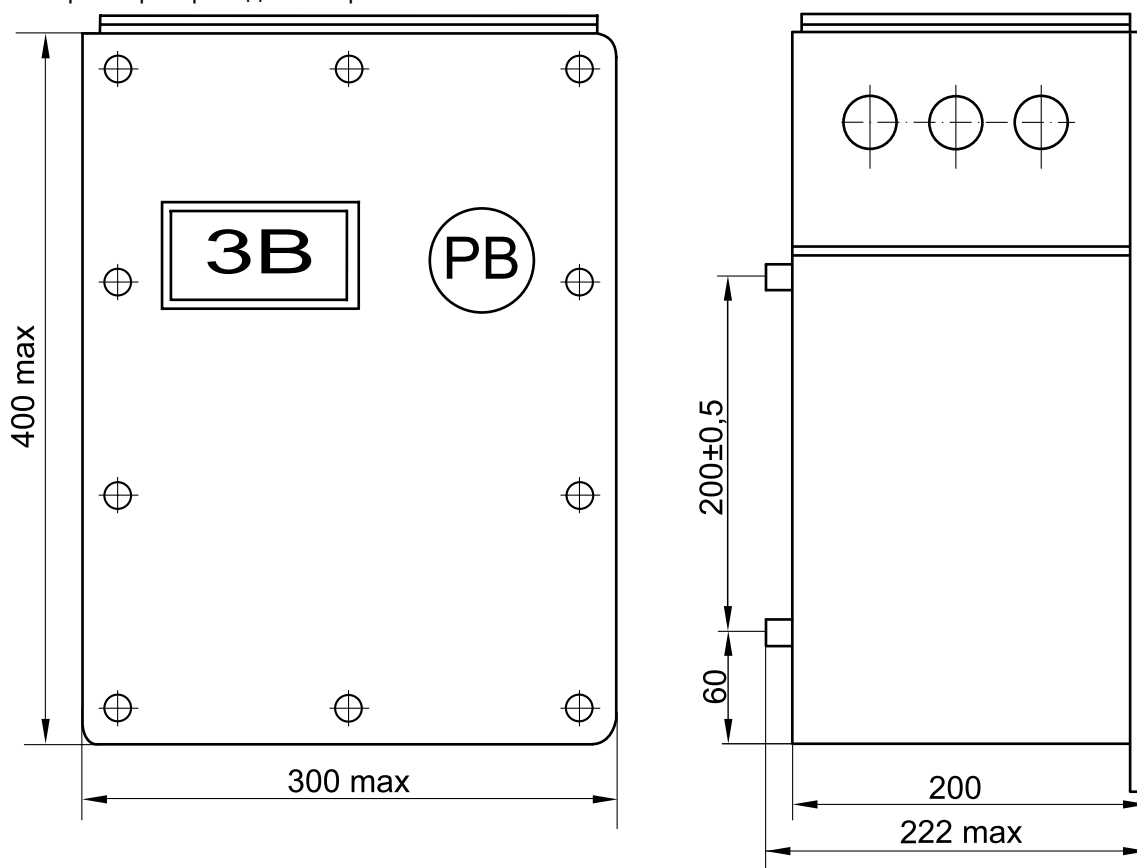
Габаритные и установочные размеры стабилизатора напряжения СНВ–2М
